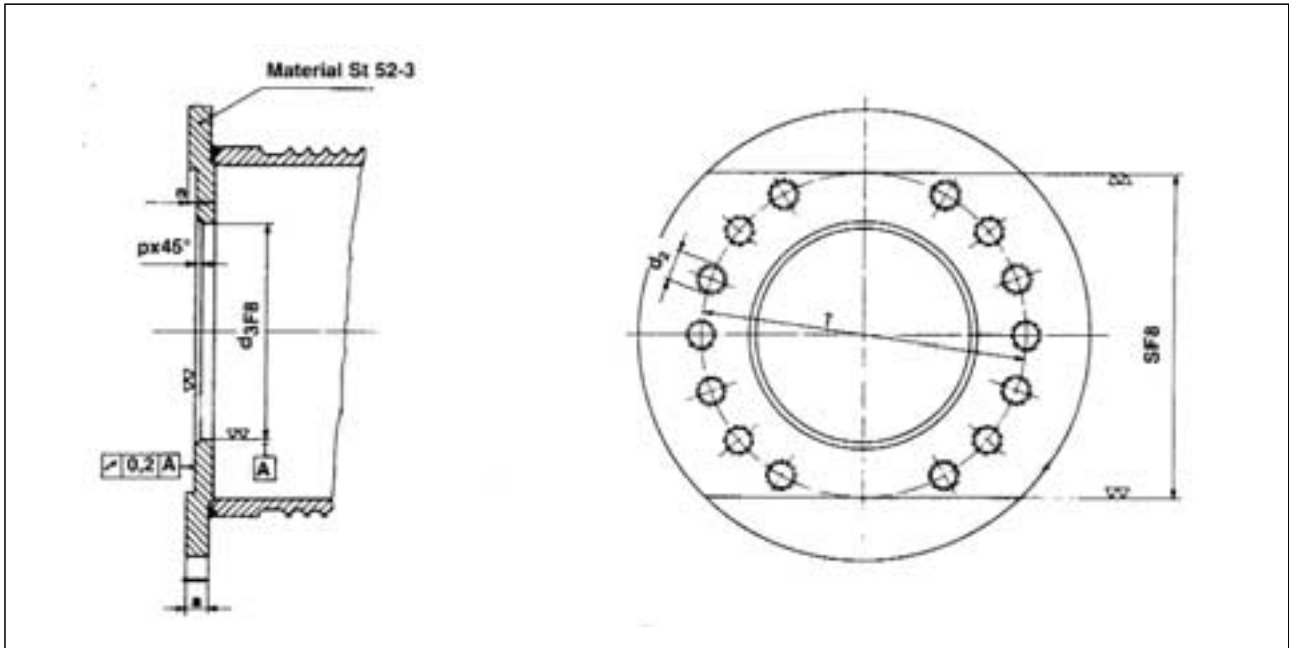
Brida lado acoplamiento para tambor de cable
